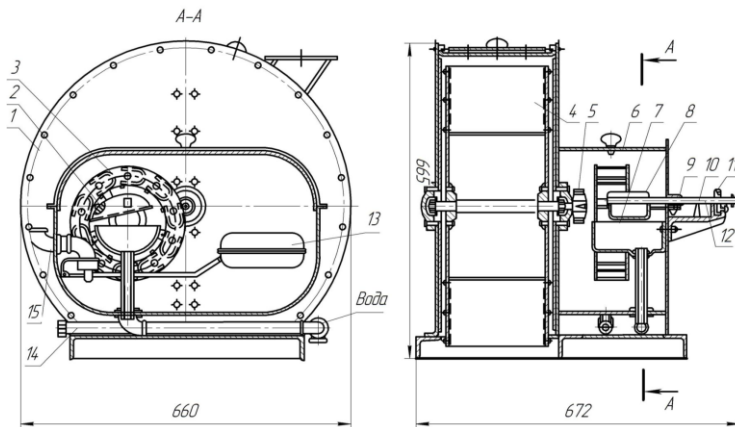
Водоструминна машина 33М-2: 1 – корпус; 2 – зубчасте колесо; 3 – водяне колесо; 4 – зернове колесо; 5 – шестірня, 6 – резервуар; 7 – нерухома посудина; 8 – рухома посудина; 9 – стержень; 10 – покажчик; 11 – шайба; 12 – рухома шкала; 13 – поплавков регулятора рівня води; 14 – зливний трубопровід; 15 – підвідний трубопровід.
